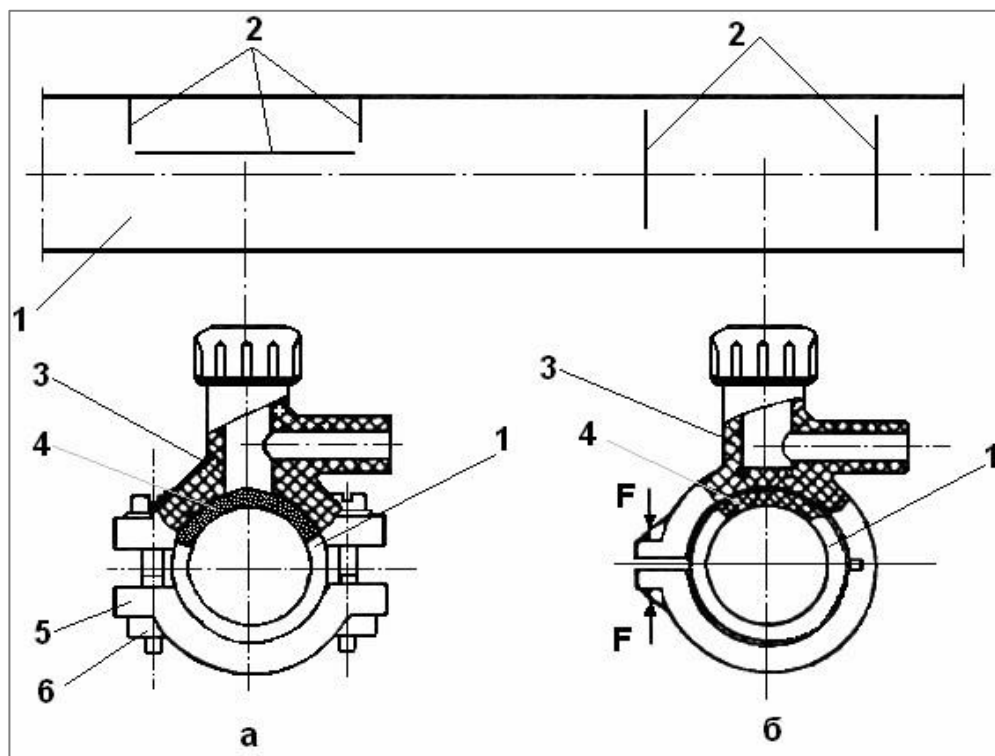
Схема сварки седловых отводов с закладными нагревателями с трубой:
